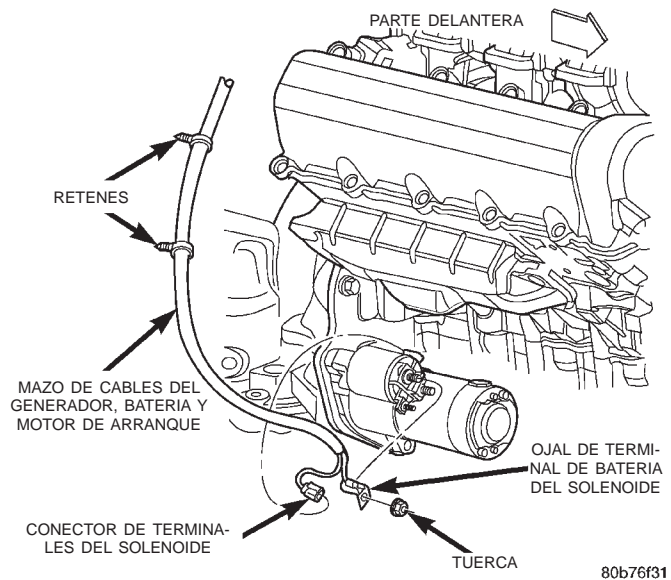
Desmontaje e instalación de mazos de cables del motor de arranque-motor 4.7L
